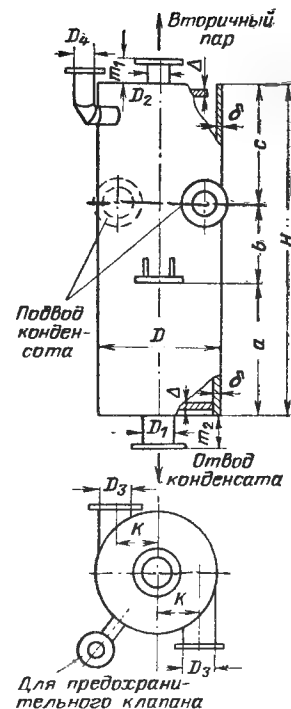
Расширительный бачок конструкции Теплоэлектропроекта.
